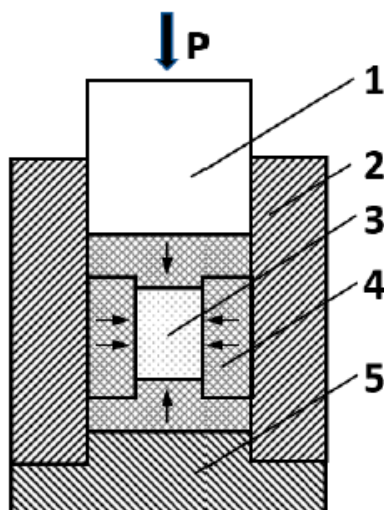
Схема цилиндрического пресса для квазиизостатического прессования: 1 - пуансон; 2 - матрица; 3 - порошок цилиндрической формы; 4 - эластомер; 5 – основание
